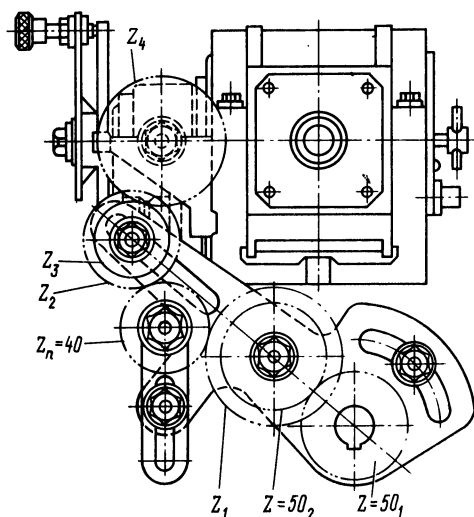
Гитара сменных зубчатых колес для фрезерования винтовых канавок
